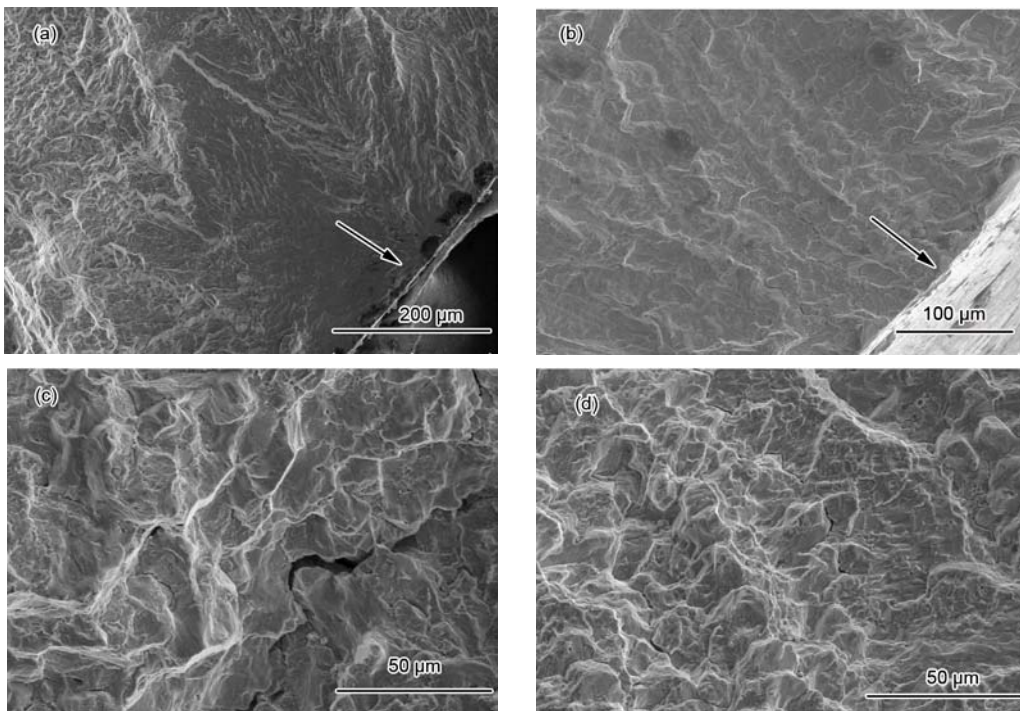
Inconel 625 合金焊接接头在 760 °C 下的低周疲劳裂纹萌生和扩展区的微观形貌
